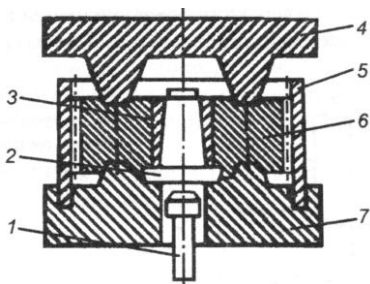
Приспособление для выдавливания в штамп:
